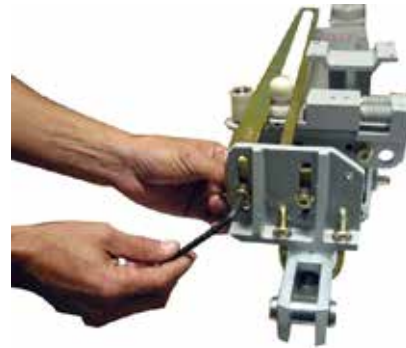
Desmontagem do Posicionador do ACP do Cilindro
